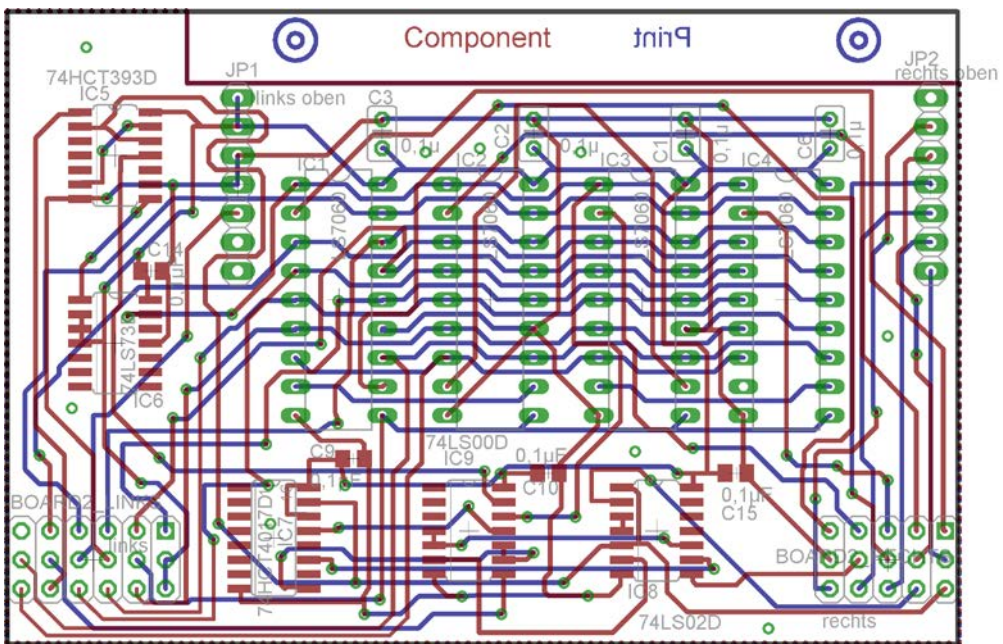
Schaltbild Abalaufsteuerung Baugruppe 2
